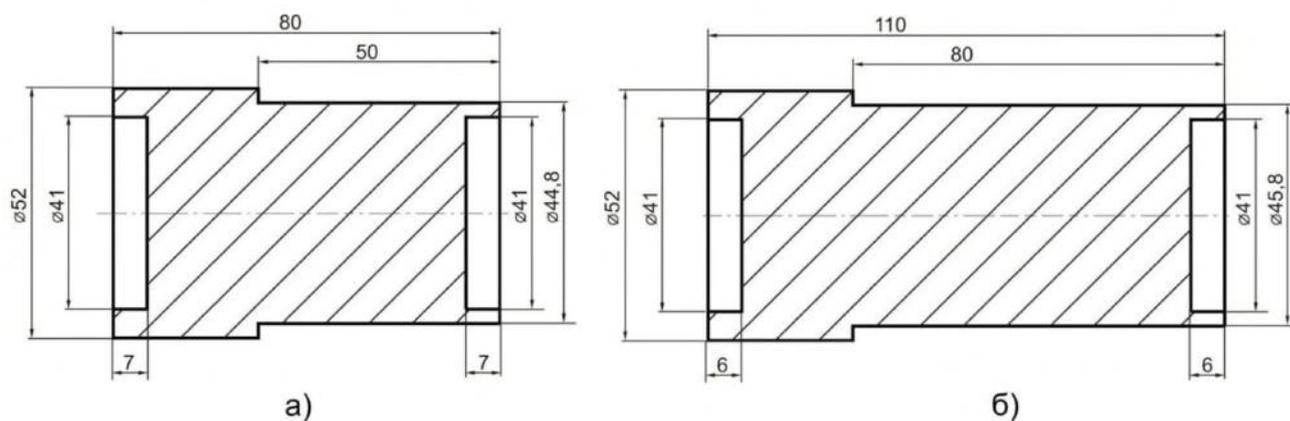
Оправки для выпрессовки и запрессовки сайлентблоков рычагов подвески: а) – верхнего рычага; б) - нижнего рычага
